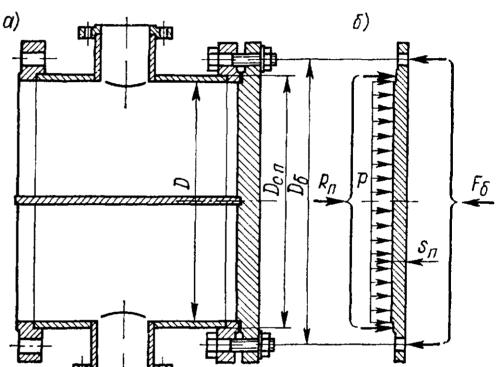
Распределительная камера горизонтального кожухотрубчатого конденсатора (а) и расчетная схема ее плоской крышки (б)
